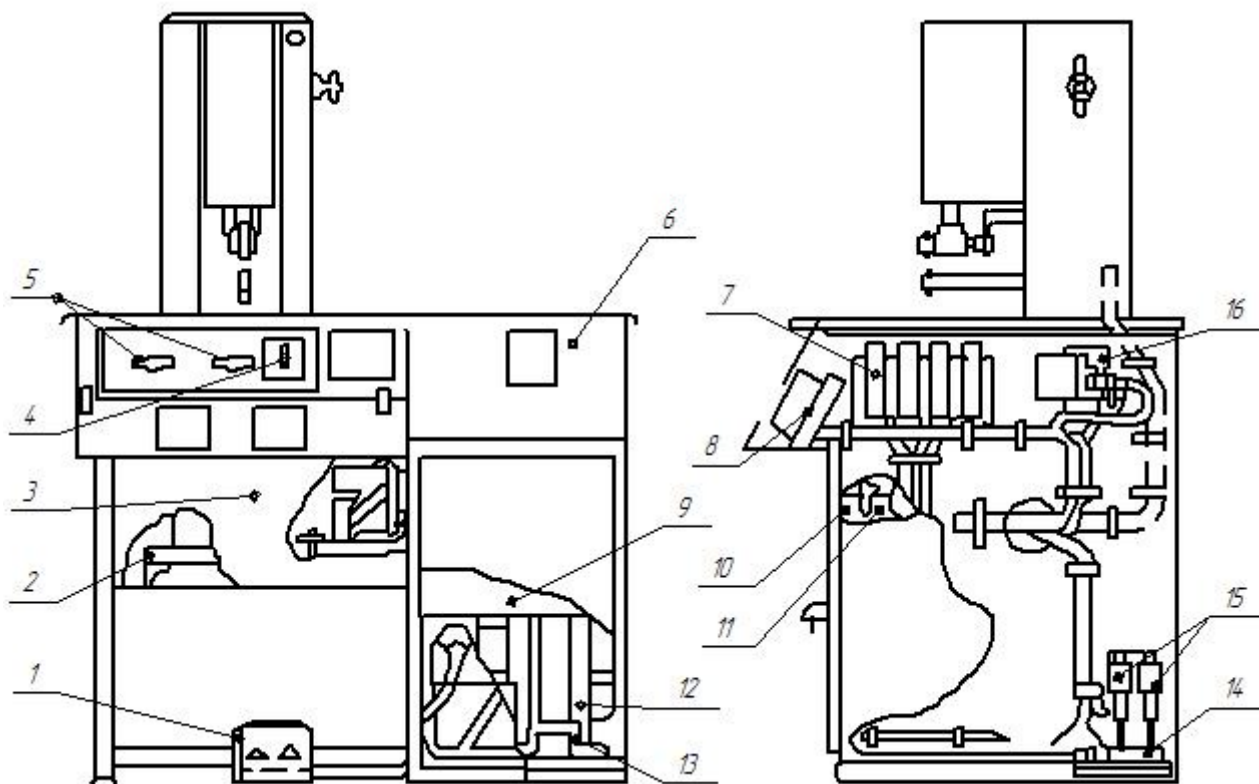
Будова машини для шовного контактної зварювання
